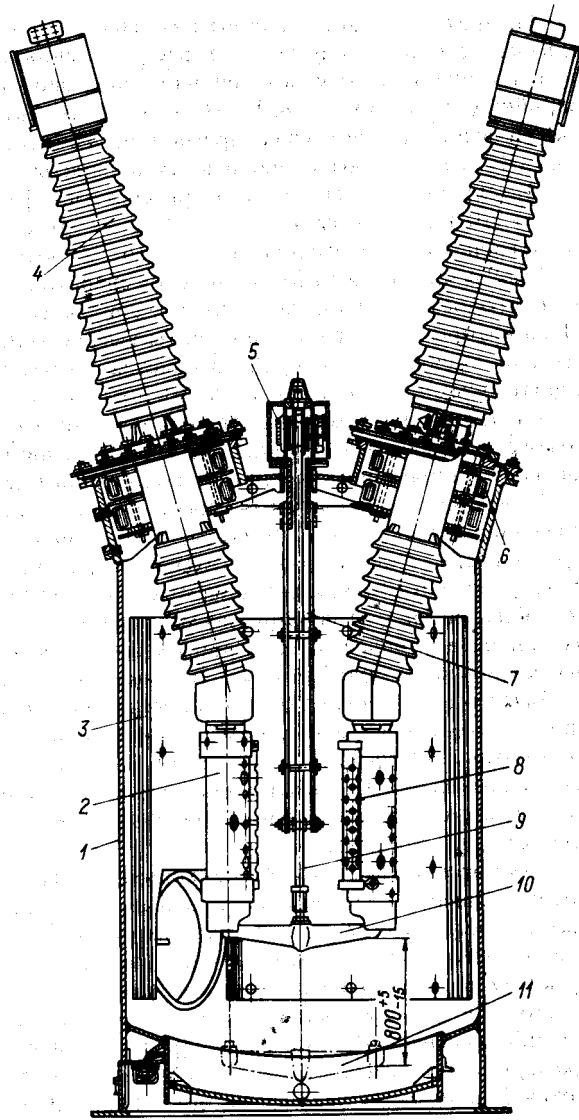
Полнос масляного бакового выключателя на 220 кВ, 1 - бак; 2 — дугогасительная камера с неподвижными контактами и шунтирующим резистором; 3 — изоляция бака; 4 — ввод; 5 — приводной механизм; 6 - трансформатор тока; 7 — направляющее устройство; 8 — шунтирующий резистор; 9 — изоляционная тяга; 10 — траверса с подвижными контактами; 11 — положение траверсы после отключения
